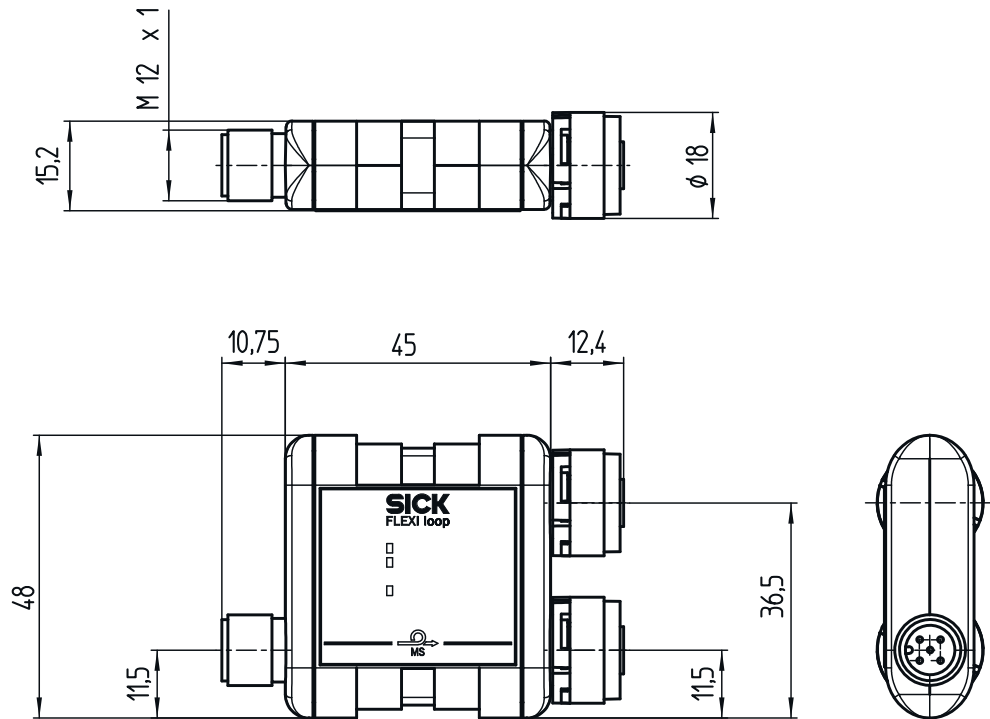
Plan coté nœud Flexi Loop (mm)
